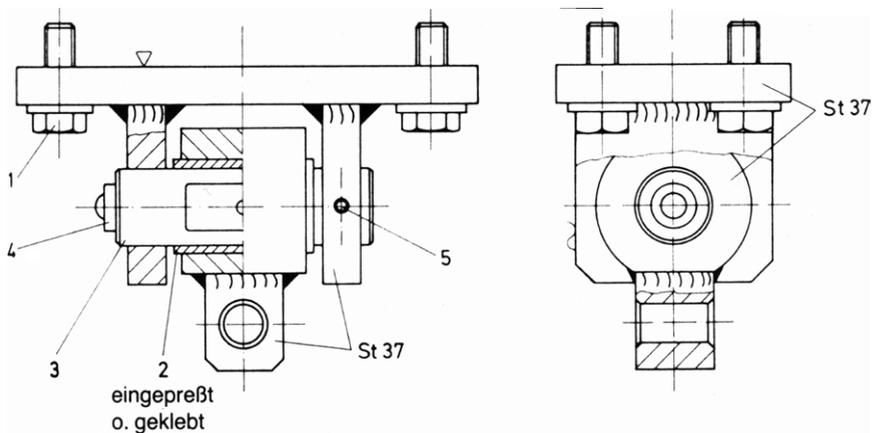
Hängelager in geschweißter Ausführung [4]
